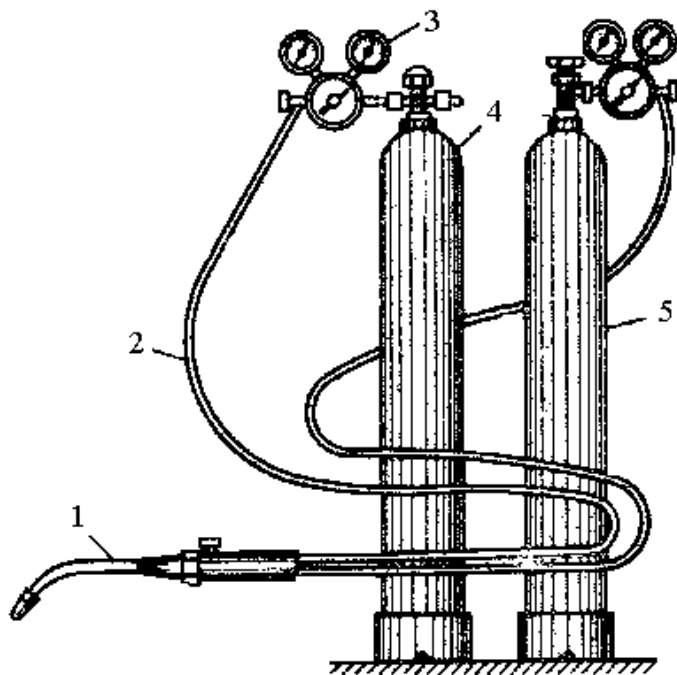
Схема газосварочного поста с питанием от баллонов: 1 - сварочная горелка; 2 - гибкий шланг; 3 - редуктор; 4 - баллон с ацетиленом; 5 - баллон с кислородом
